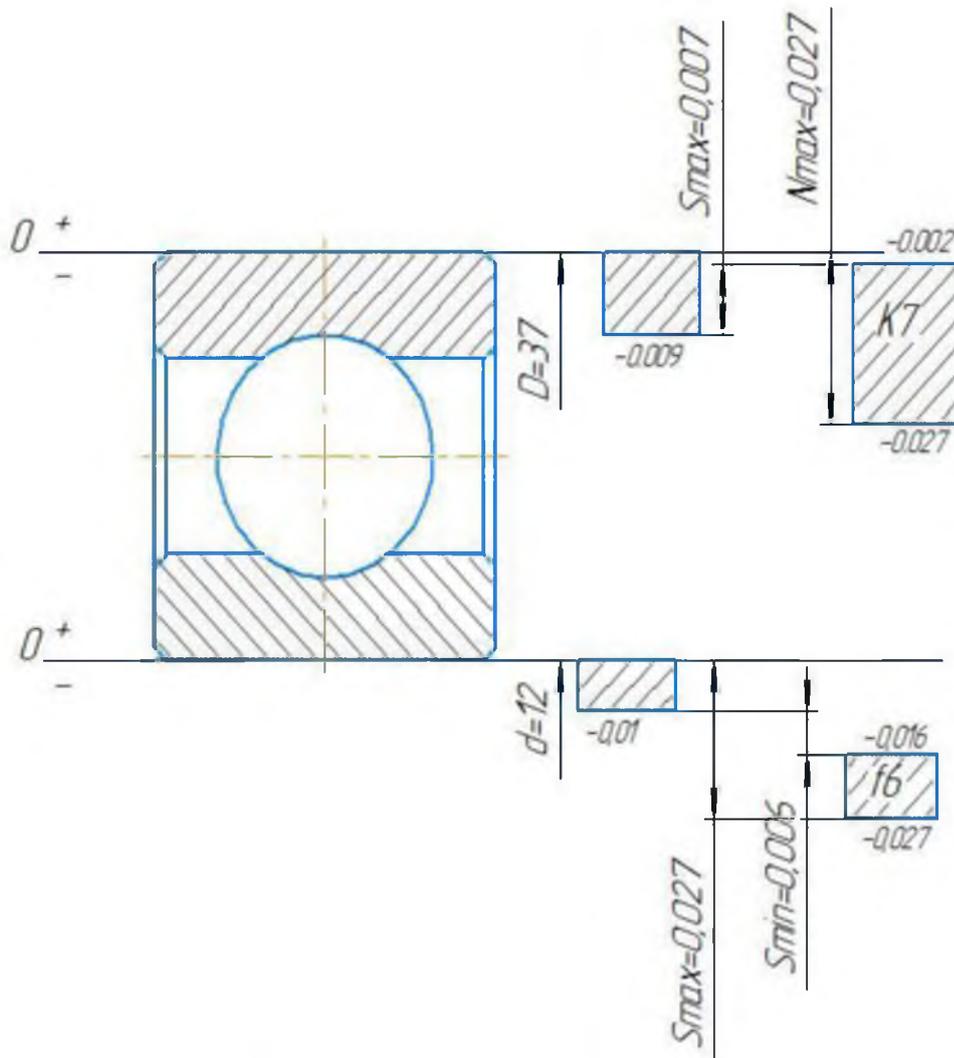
Схема расположение полей допусков колец подшипника и сопрягаемого с ним вала и отверстия в корпусах
